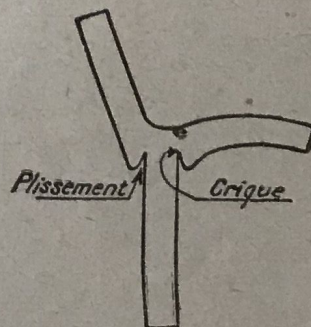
Forgeage d'un Té par ouverture des branches.
